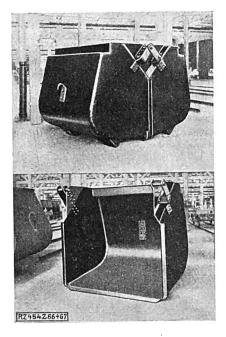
und 67 Geschweißte Kohlengreifer
